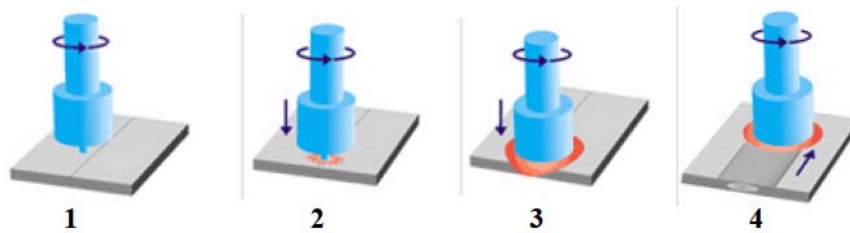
representação esquemática do processo FSW – Friction Stir Welding. Fonte: Rodriguez et al, 2013 P.4.
